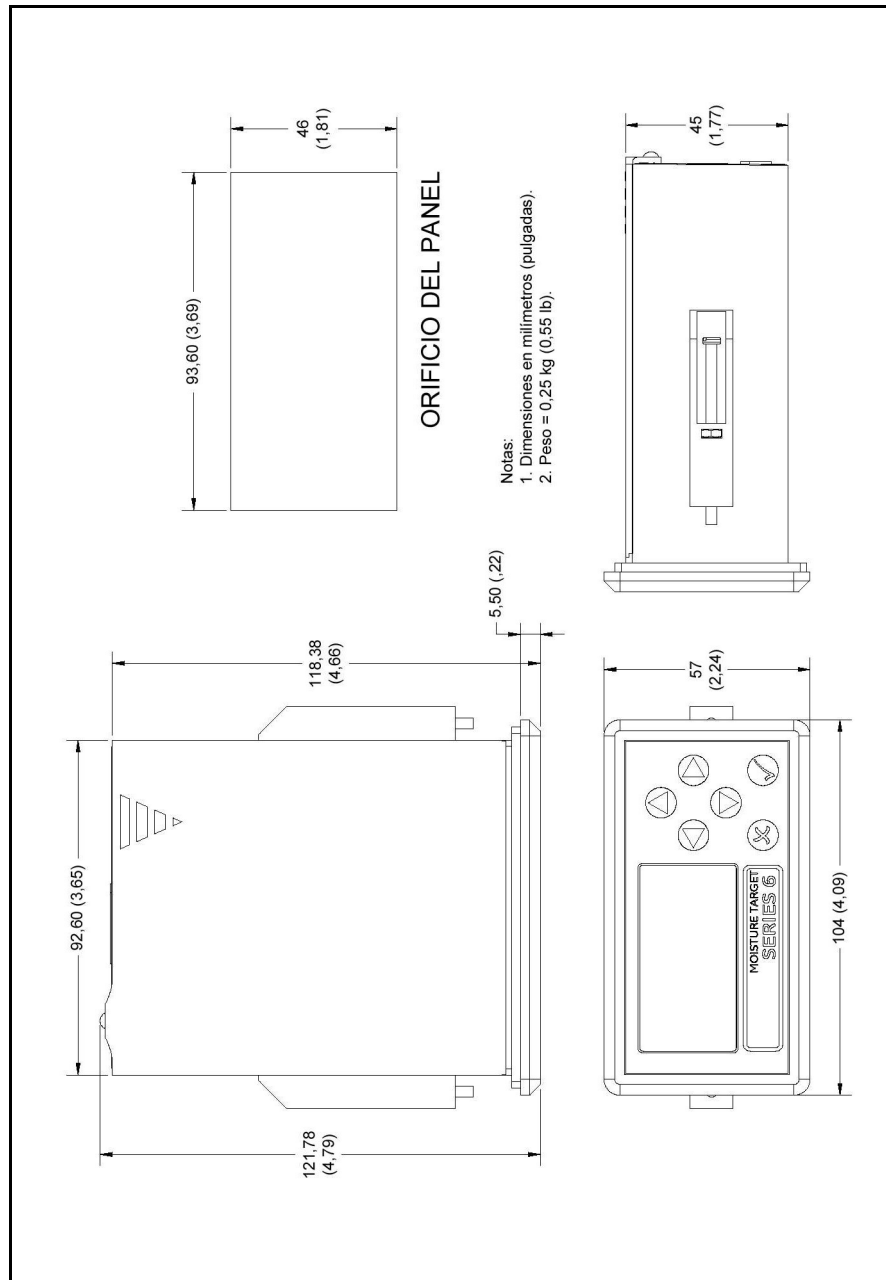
Croquis y plano de montaje (plano n.º 712-1550)
